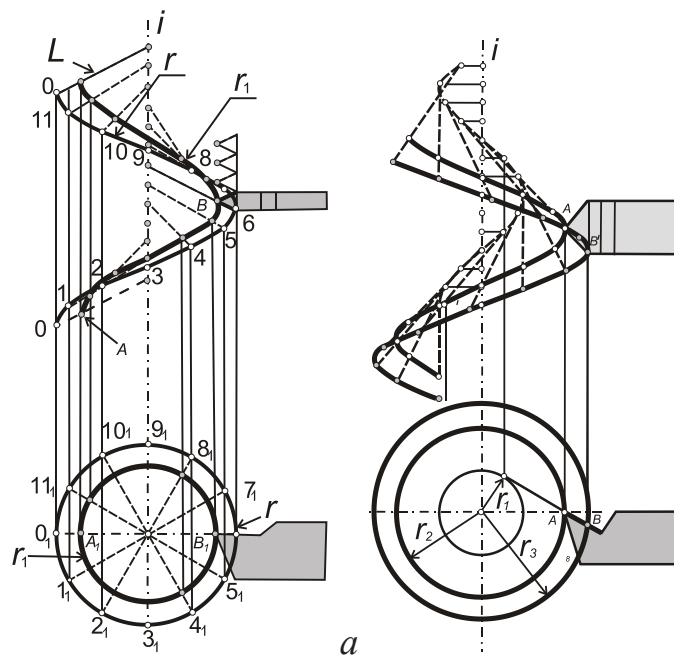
Схема виготовлення токарним різцем гвинтових поверхонь
